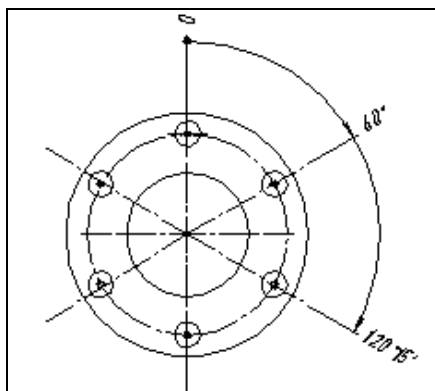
Простановка угловых размеров с общей размерной линией
